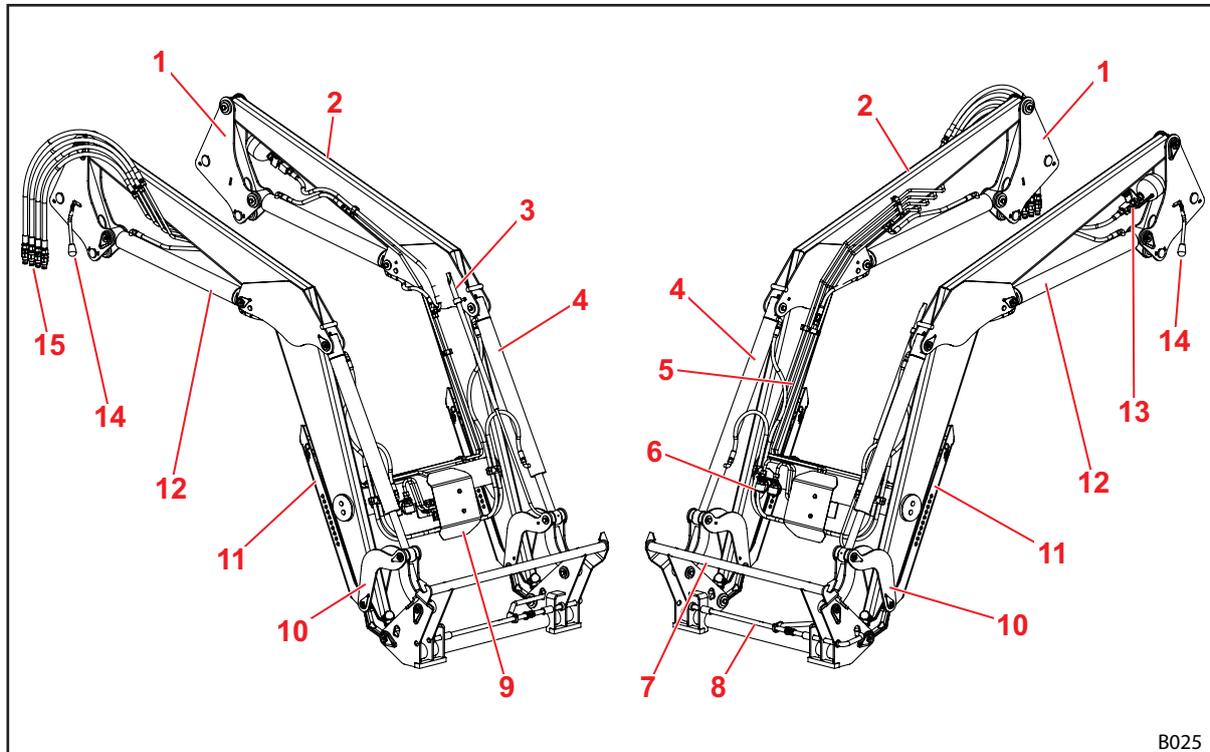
Caricatore frontale H (senza guida parallela meccanica)
